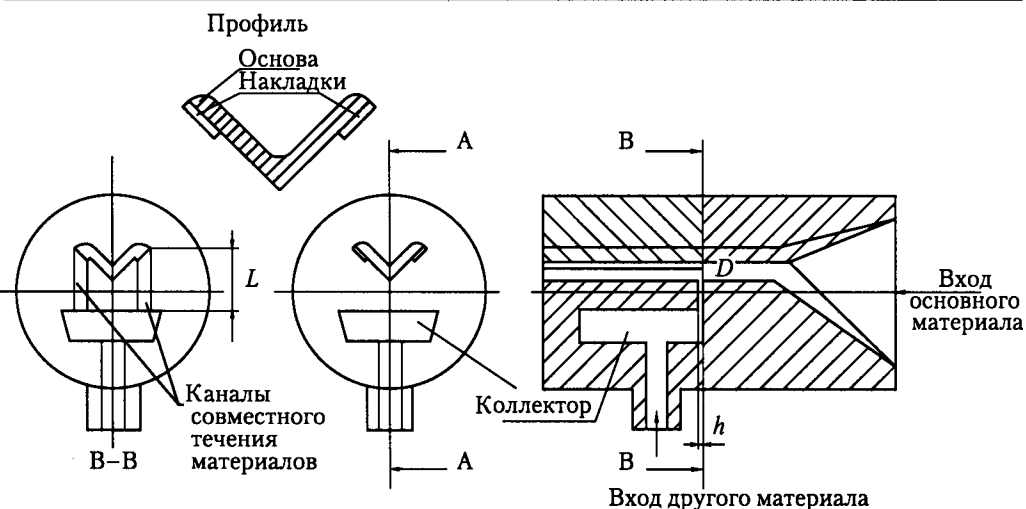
Схема экструзионной головки для изготовления двухслойного комбинированного профиля [32]
